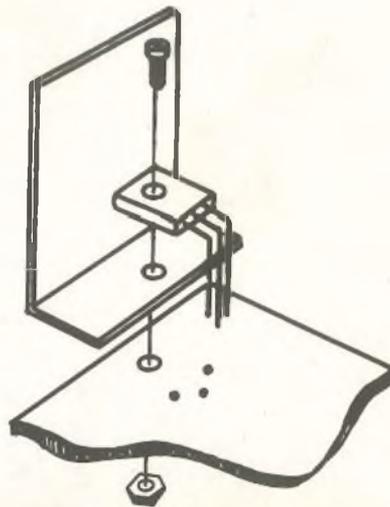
Vista da montagem do transistor de saída em seu dissipador.
